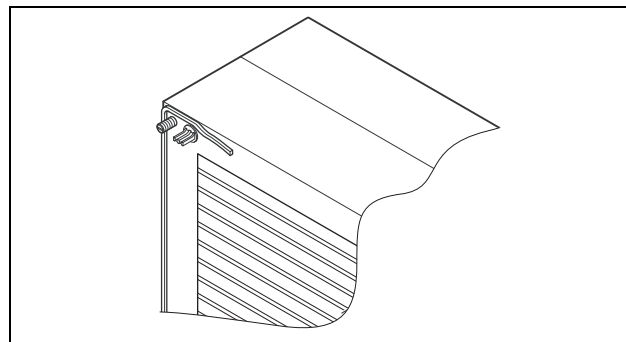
Наклеивание уплотнительной ленты на кожух корпуса
